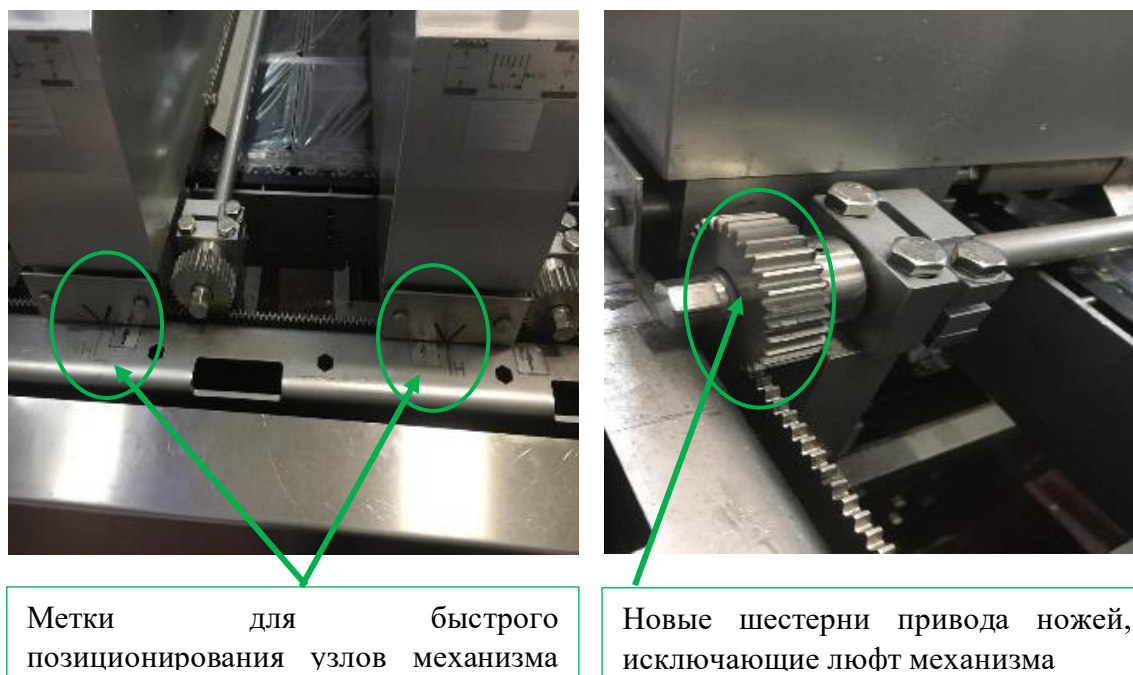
Маркировка положения узлов механизма привода ножей и новые шестерни привода.
